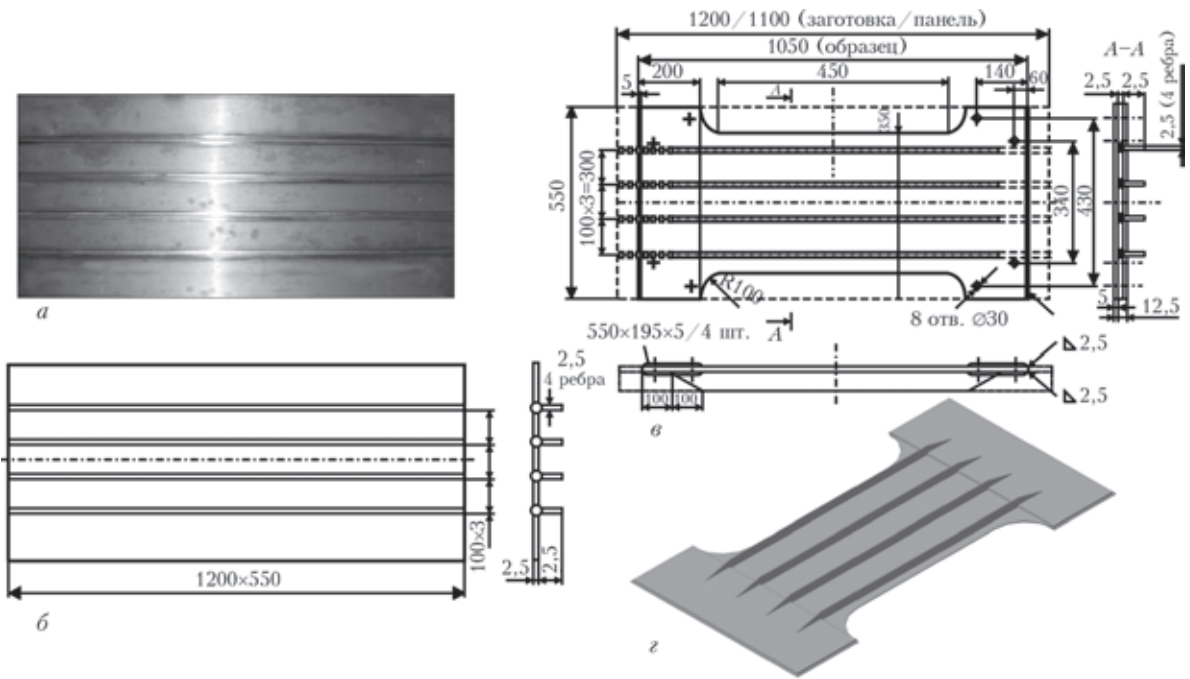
Сварная ребристая панель из сплава ВТ20 второго этапа исследований: *а* — общий вид; *б* — эскиз панели; *в* — эскиз образца лопаточного типа; *з* — общий вид образца для испытаний на усталость
